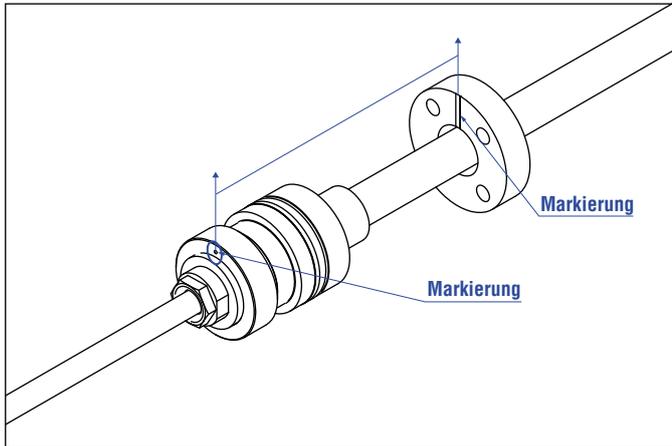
Magnetausrichtung eines Ringmagneten für RDV EtherNet/IP™ mit interner Linearisierung am Beispiel eines »S«-Flansches
